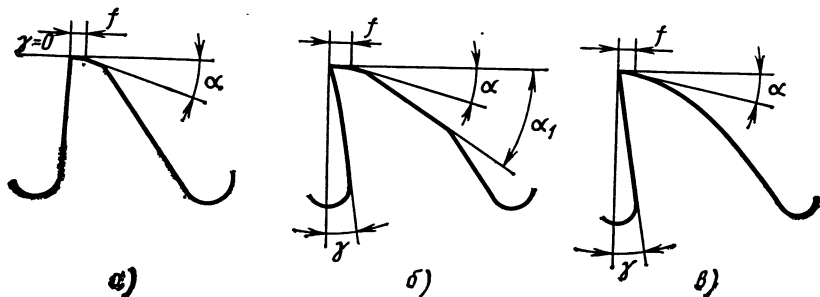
Формы зубьев фрез из инструментальных сталей:
